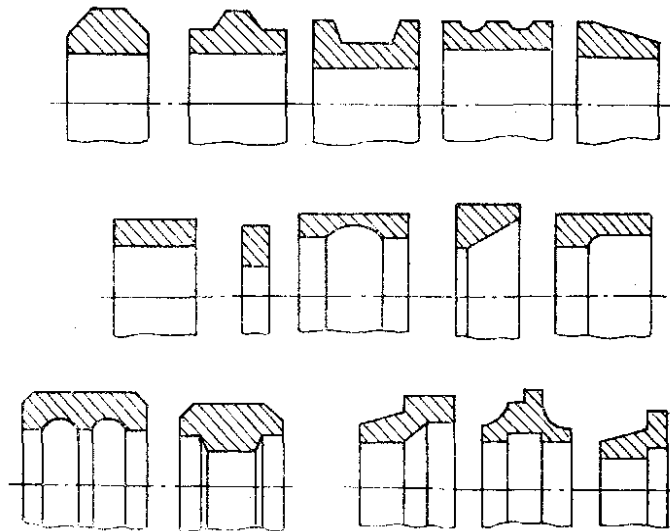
Форми січень кільцевих заготовок виготовлених розкатуванням
